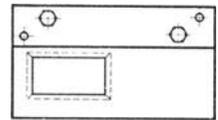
Einseitige Querführung für sperrige Werkstücke.
